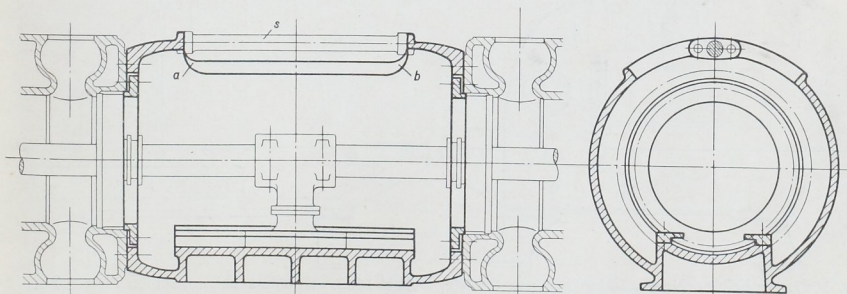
Zwischenstück mit Ausschnitt oben.
